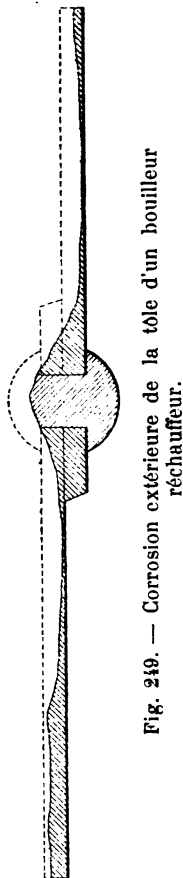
Corrosion extérieure de la tôle d'un bouilleur réchauffeur.
